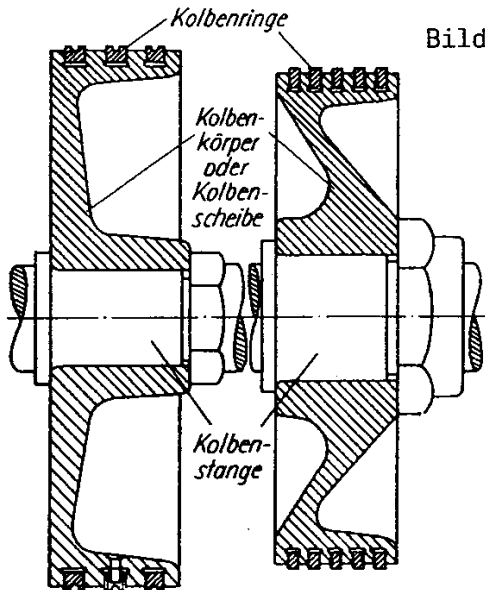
Dampfkolbenquerschnitt alter Länderbahnlokomotiven (schwedischer Kolben)
